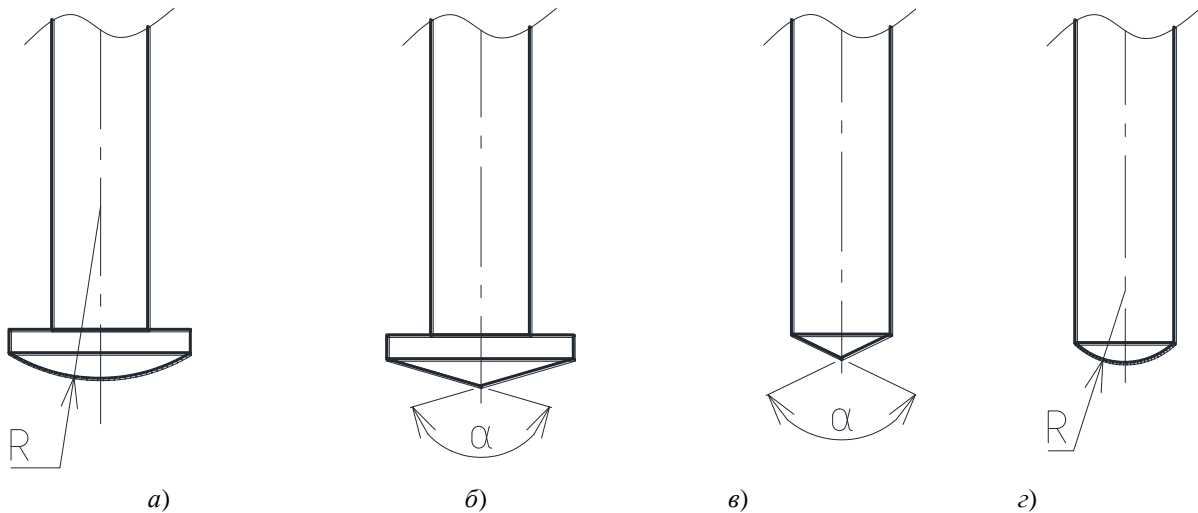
Различные формы подготовки торцов стержней под сварку
